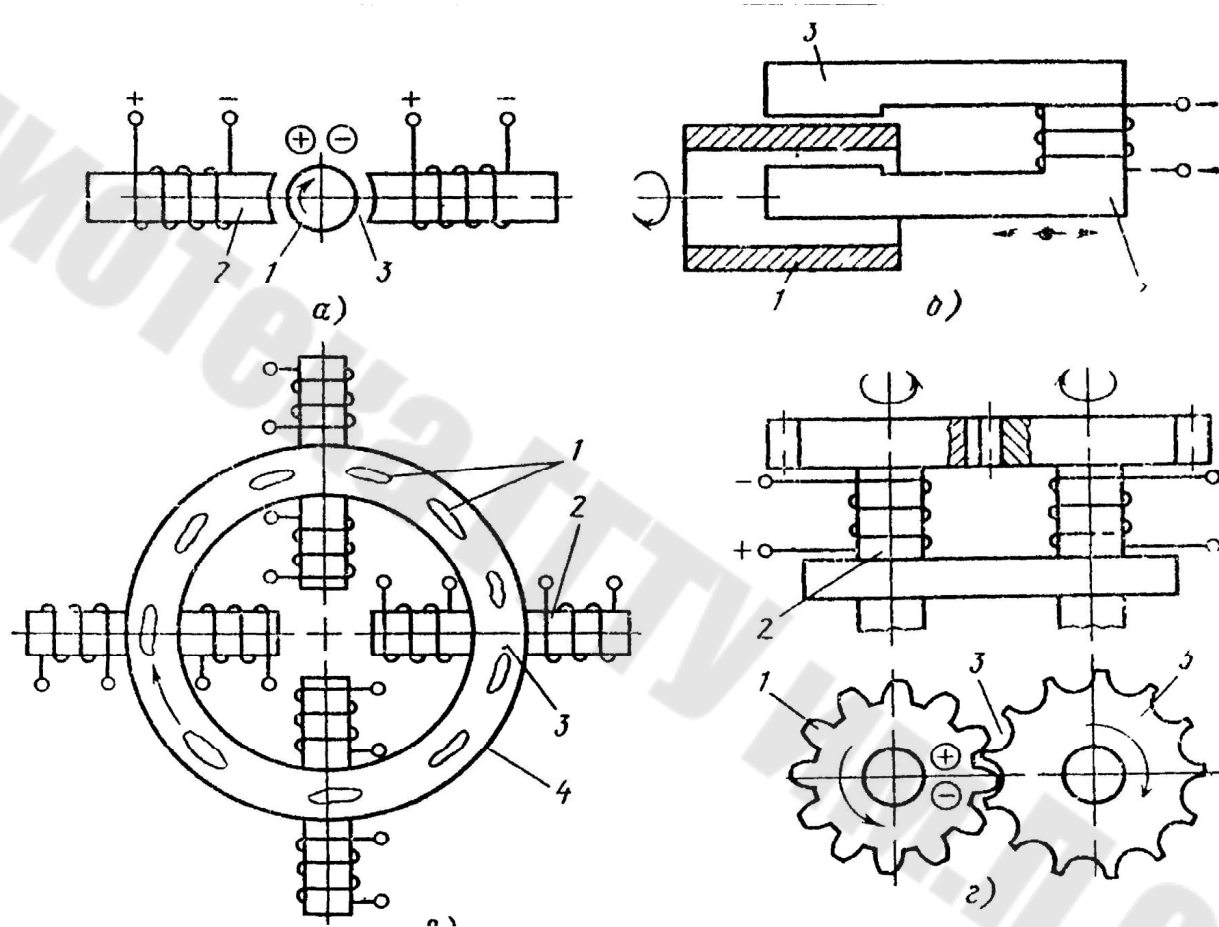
Схема МАП с использованием ферромагнитного абразивного порошка в качестве режущего инструмента и передачи движения резания обычным приводом:
